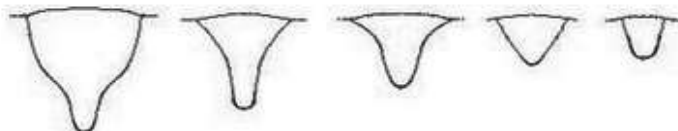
Зміна форми шва й глибини проплавлення зі збільшенням швидкості зварювання від 21,3 до 100 мм/с
